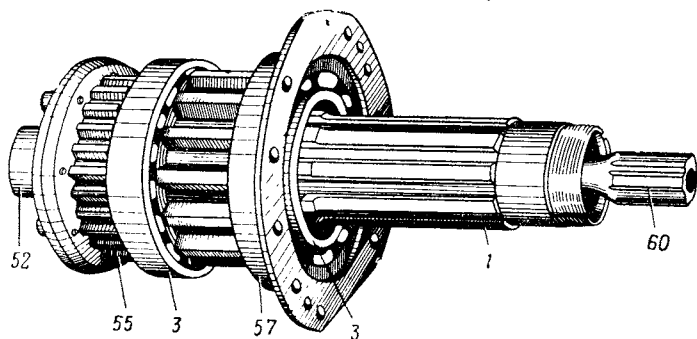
Ведущий вал в сборе (общий вид и разрез):
